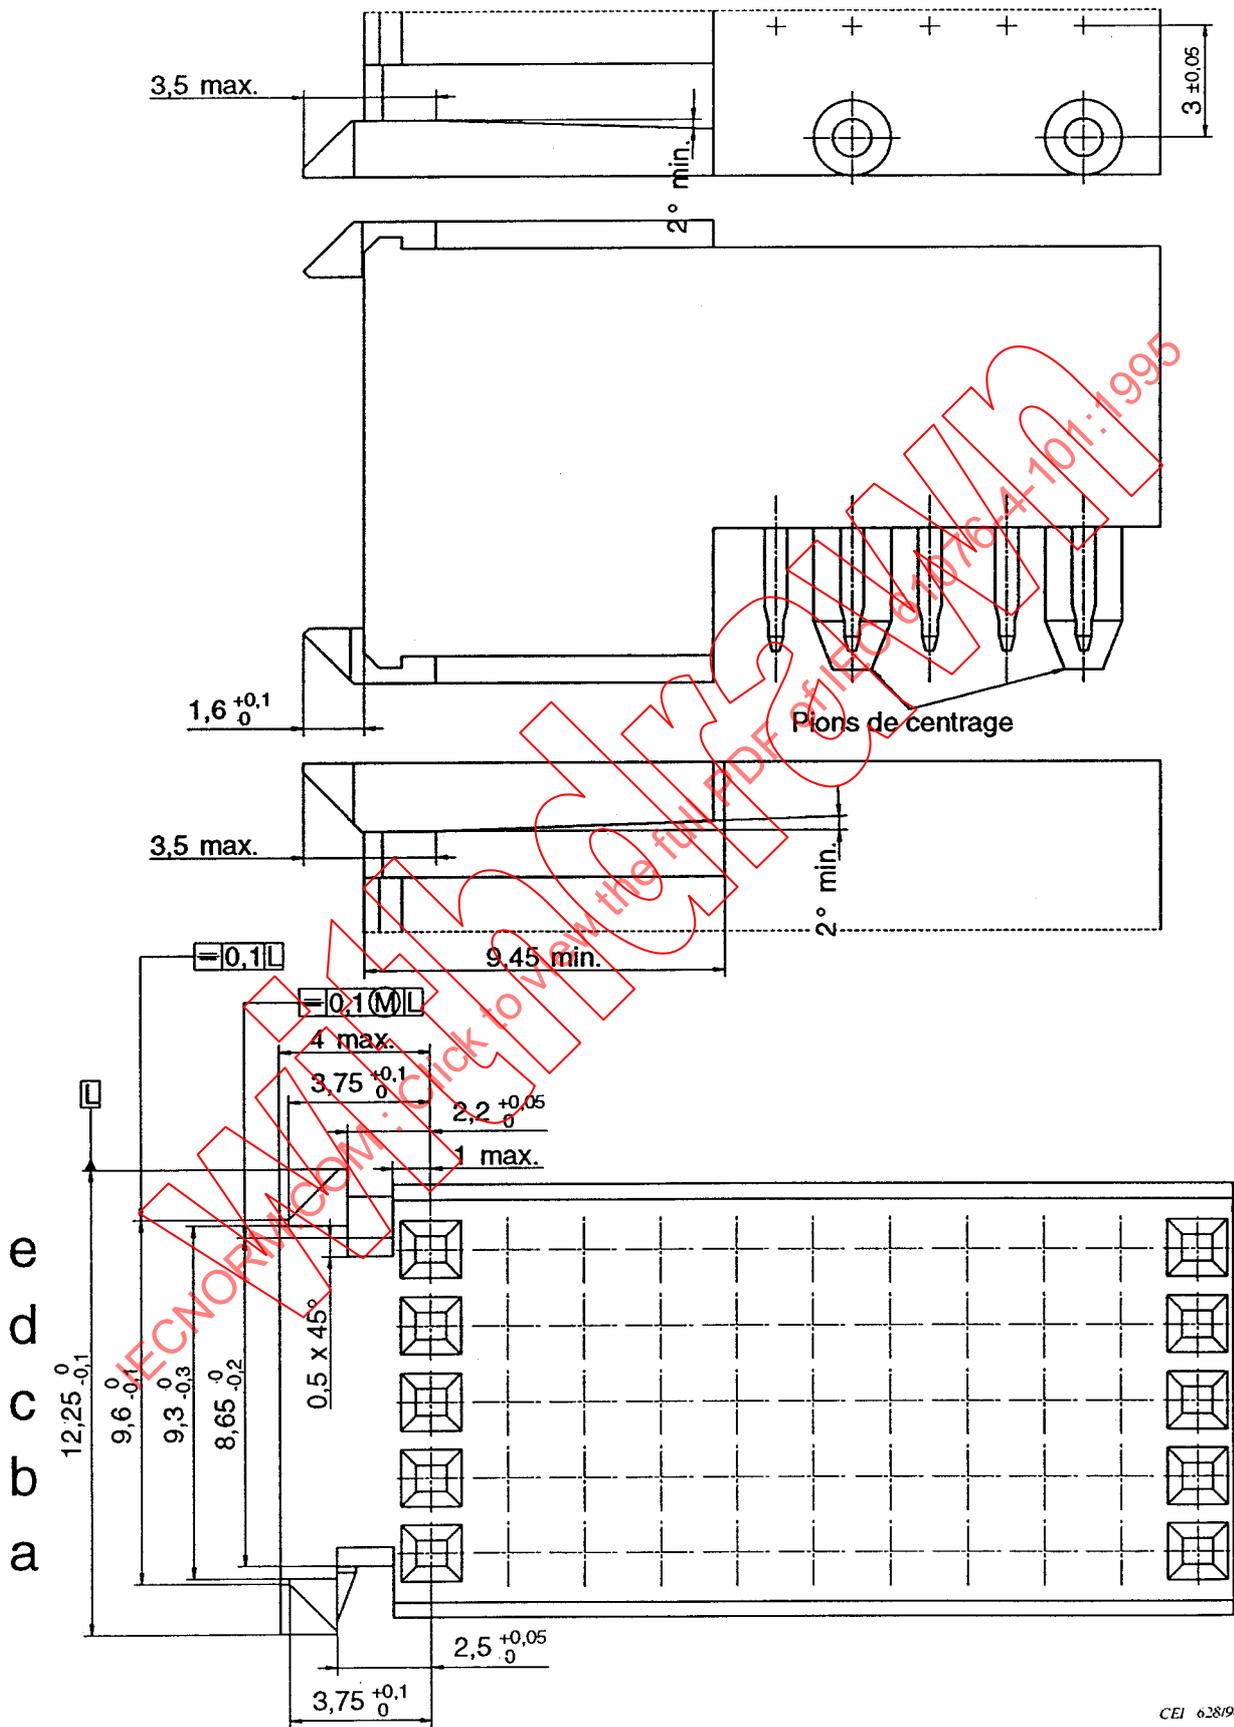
Dimensions du modèle C, module de fiche d'extension 25 mm
